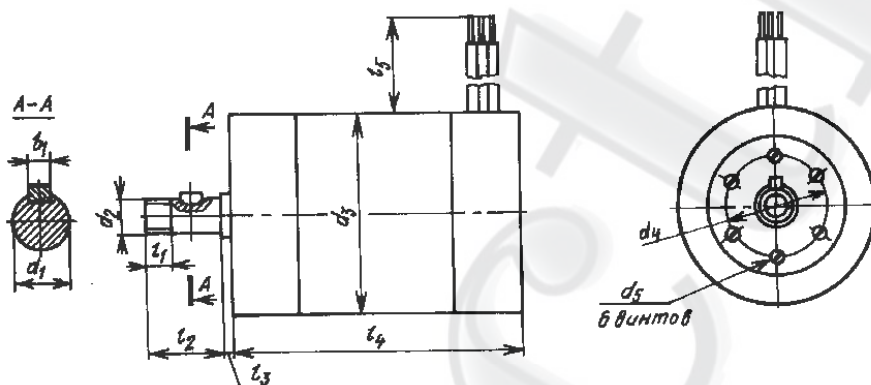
Габаритные и присоединительные размеры двигателей (исполнение с креплением на хомутах с одним свободным концом вала)
